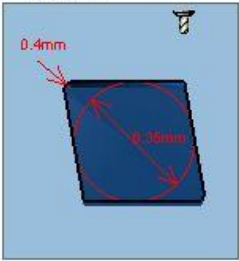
Дані про пластину TCMT 11 03 12-PR 4425
